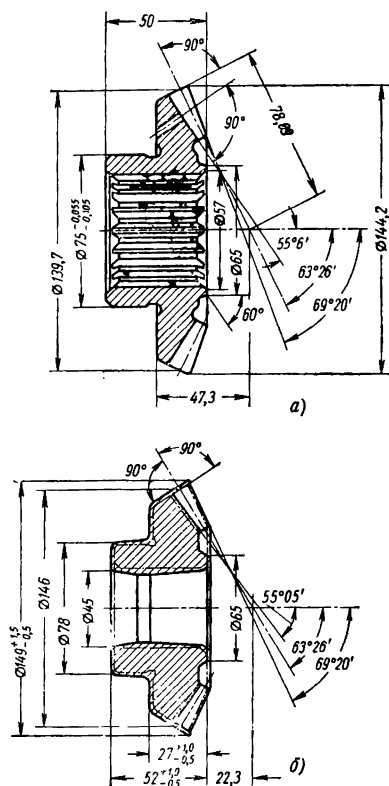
Чертежи детали (а) и поковки (б) шестерни полуоси
